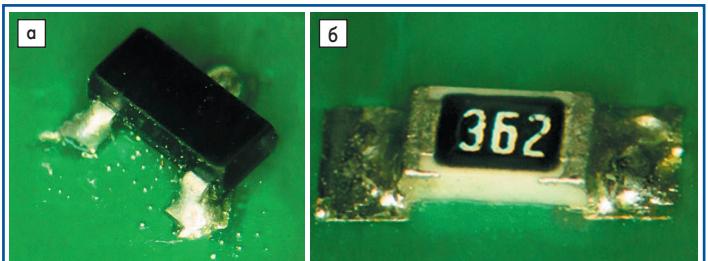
Дефекты монтажа SMD-компонентов: а) образование шариков припоя; б) недостаточное перекрытие контактных площадок
